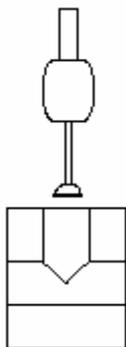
Das Werkzeug in die Bohrung einfahren, möglichst nahe an die Kreuzung der Bohrung.
